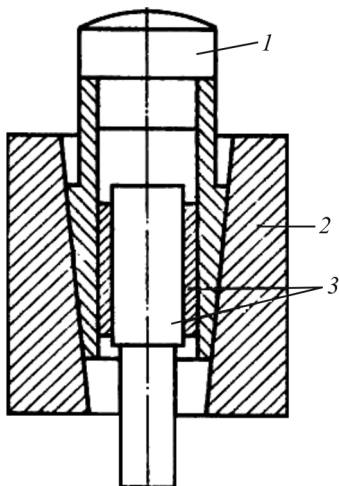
Приспособление для сварки охватывающих соединений с использованием термонатяга: 1 – конусный пуансон; 2 – оправка; 3 – свариваемые детали
